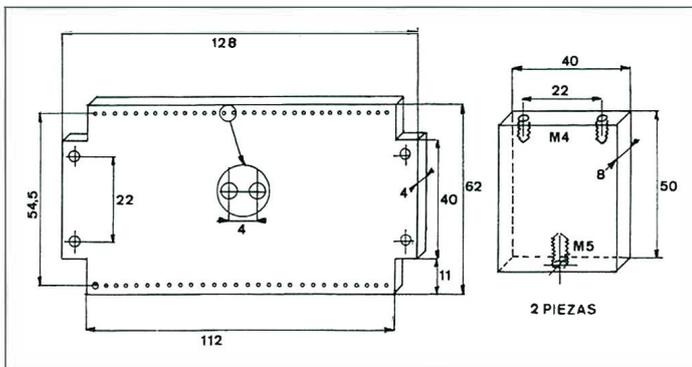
Despiece del soporte de la bobina L1 del tanque de placa. El hilo de la bobina, una vez devanado sobre una forma cilíndrica, es pasado a través de los agujeros del soporte a fin de que adquiera solidez mecánica. El hilo utilizado es de cobre plateado de 1,5 mm de diámetro, comprende 27 espiras espaciadas 2,5 mm y con un diámetro interior de 53 m/m. El material utilizado en todas las piezas es policarbonato, otros materiales plásticos como pueden ser, el PVC o el Metacrilato, se calientan con la RF. Los tornillos M4 utilizados en la unión del soporte de la bobina, son de nilón.
